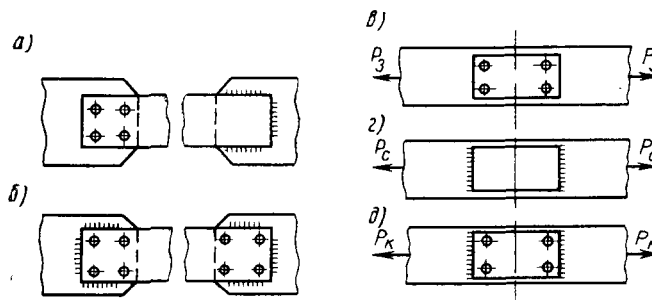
Комбинированные клепадно-сварные соединения:
